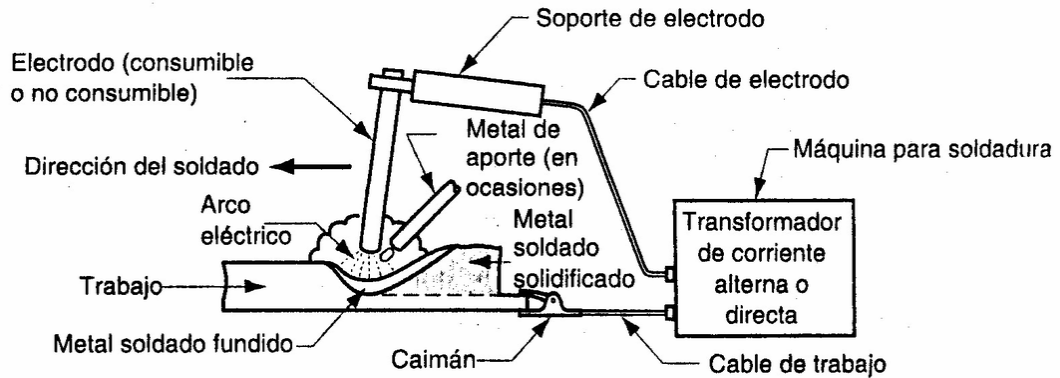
Esquema de soldadura por arco eléctrico
